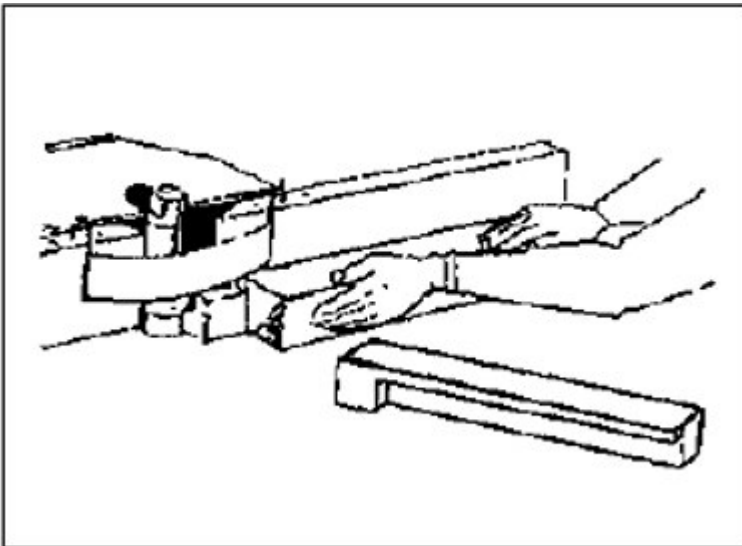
Fräsen von Werkstücken mit kleinem Querschnitt
